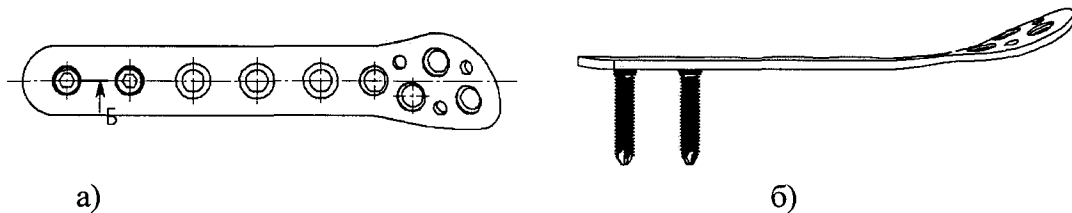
Креслення пластини-фіксатора: а – вигляд спереду; б – вигляд збоку.
